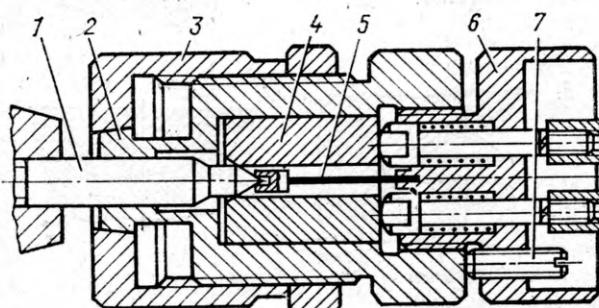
Приспособление для доводки контактного пояска на запирающем конусе иглы:
